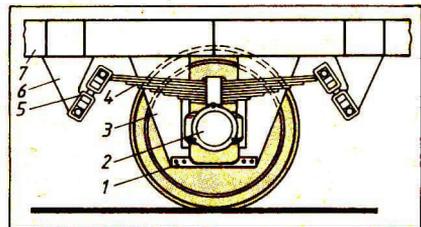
Achslagerführung durch Achshalter bei fest mit dem Wagen verbundenem Laufwerk
